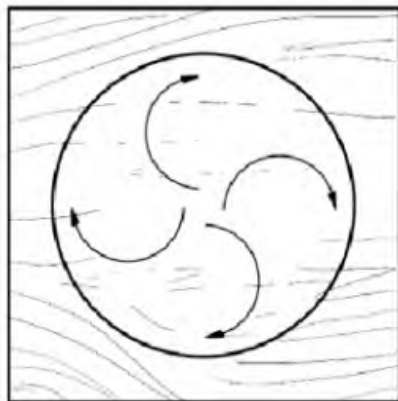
Выполнение круглой вогнутой выемки на торце заготовки вторым способом изогнутыми линиями (стрелками показано направление движения инструмента)
